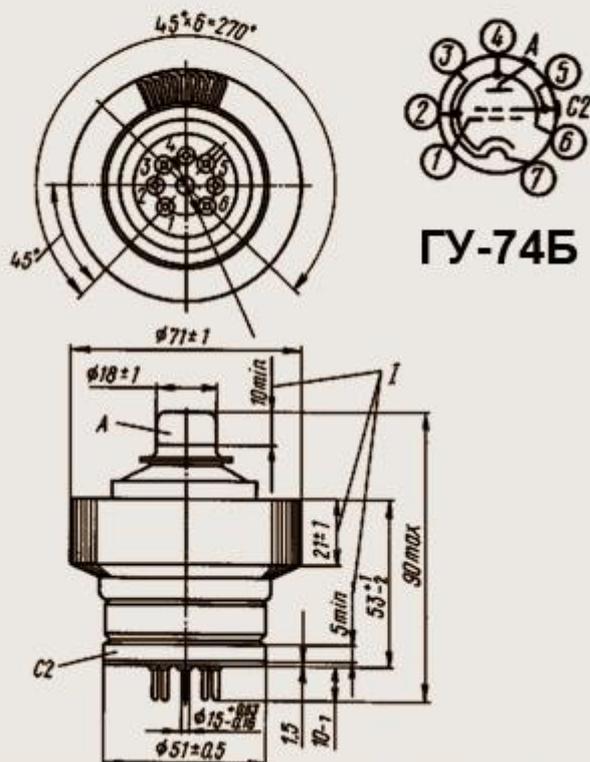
Габаритные и присоединительные размеры генераторного тетрода ГУ-74Б.
